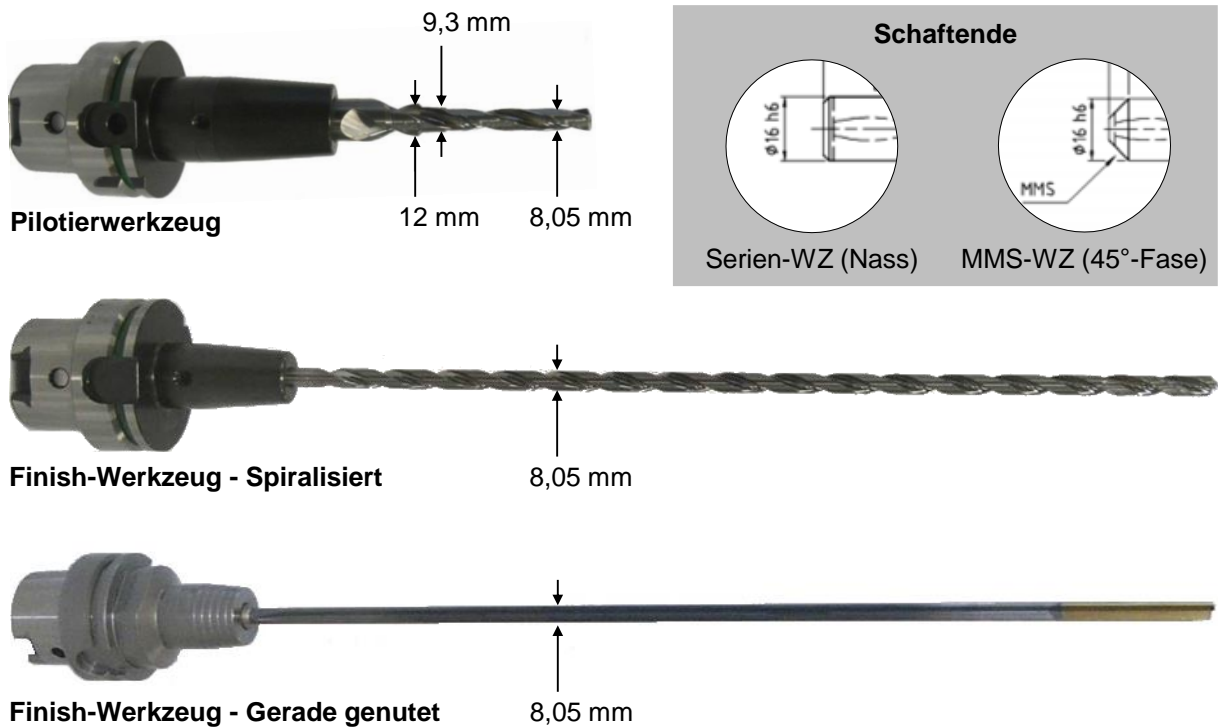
Finaler Stand der MMS-Werkzeuge für die Bearbeitung des Hauptölkanals im ZK N20
